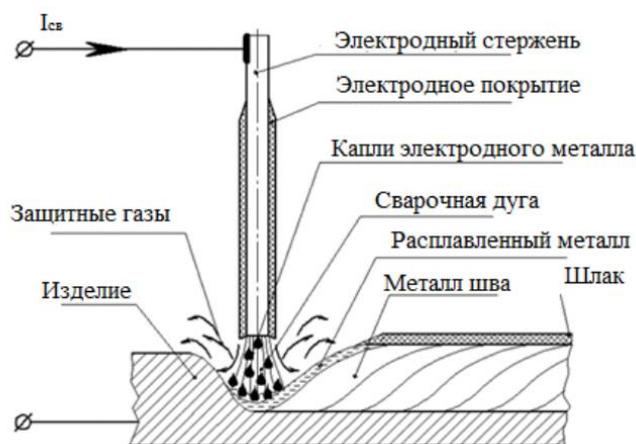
Схема дуговой сварки покрытым электродом
